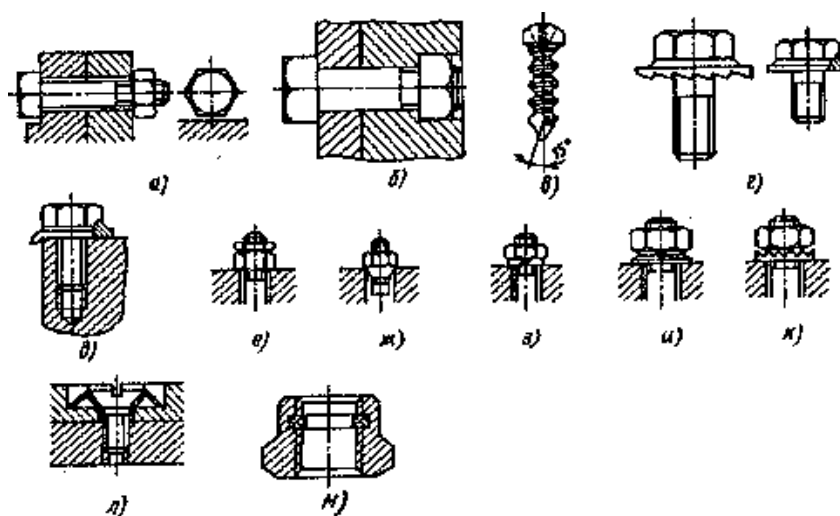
Примеры технологичных конструкций резьбовых соединений и крепежных деталей
